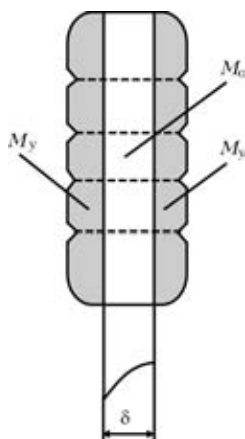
Схема валика, наплавленного на узкую подложку многослойной наплавкой: M_0 — зона чистового размера восстановленной поверхности; M_y — зона боковых усилений наплавленного валика
